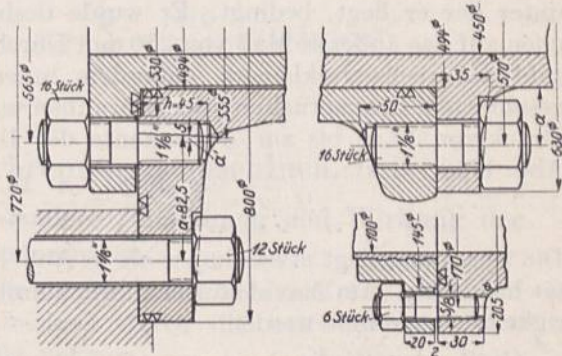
bis 1758. Flanschverbindungen am Zylinder Abb. 1755. M. 1:5. Abb. 1756. Anschluß am Rahmen und Verschraubung des vorderen Deckels. Abb. 1757. Verschraubung der Köpfe mit dem Laufzylinder. Abb. 1758. Anschluß des Zuleitungsrohres.
